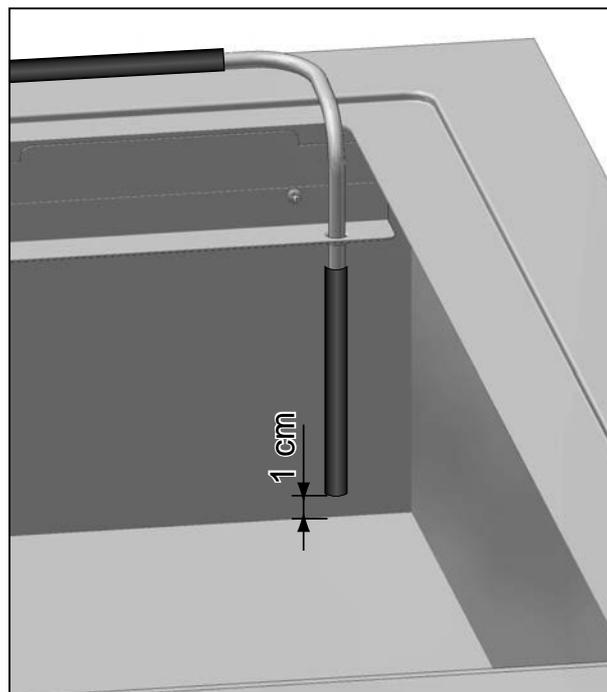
Glisser un segment de tuyau sur le tube d'aspiration et couper à la bonne hauteur
